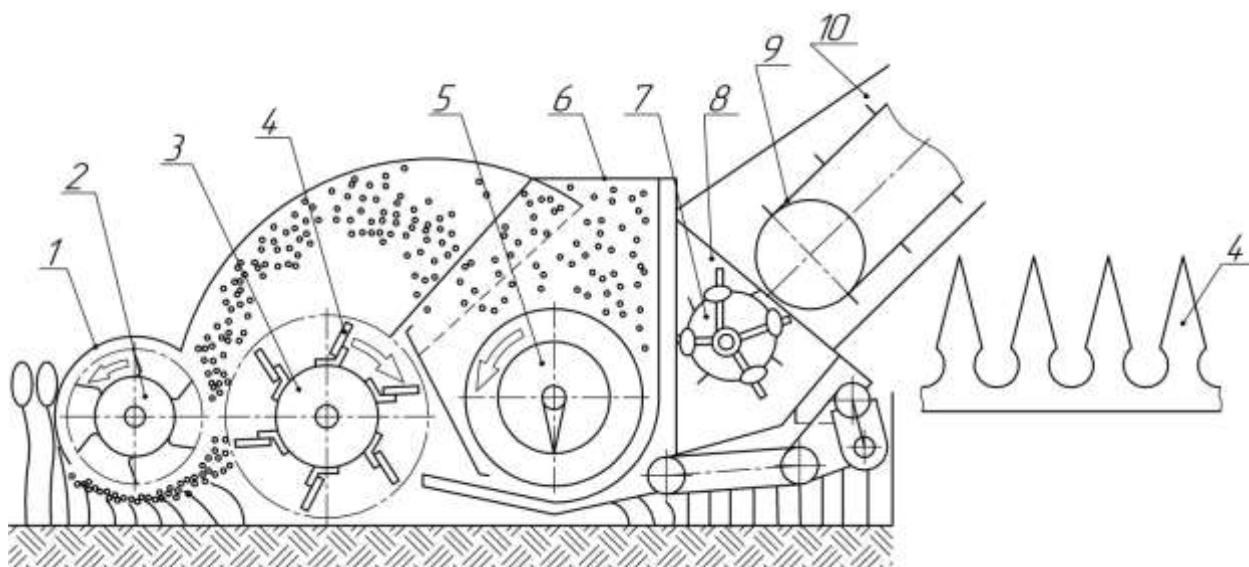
Принципиальная схема работы двухбарабанной очесывающей жатки: 1 – кожух; 2 – подающий барабан; 3 – очесывающий барабан; 4 – гребенка; 5 – шнек; 6 – платформа; 7 – битер; 8 – проставка; 9 – плавающий транспортер; 10 – наклонная камера
